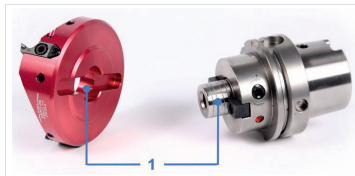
Werkzeug und Hydrodehnspanndorn reinigen
